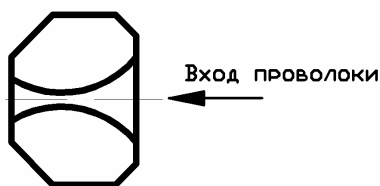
Схема финишной операции при изготовлении часовых камней
